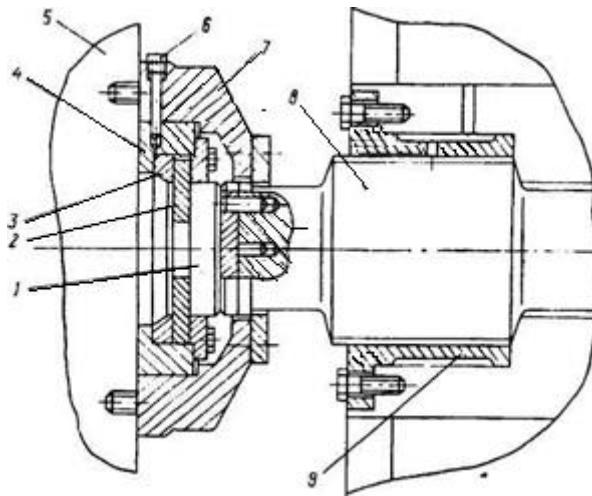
Запобіжний пристрій механізму регулювання зазору:
